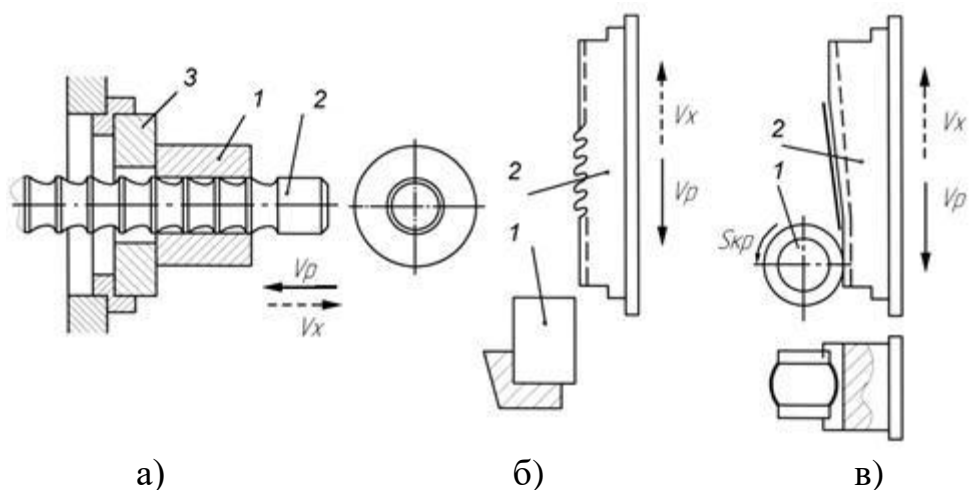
Схемы обработки поверхностей на протяжных станках
